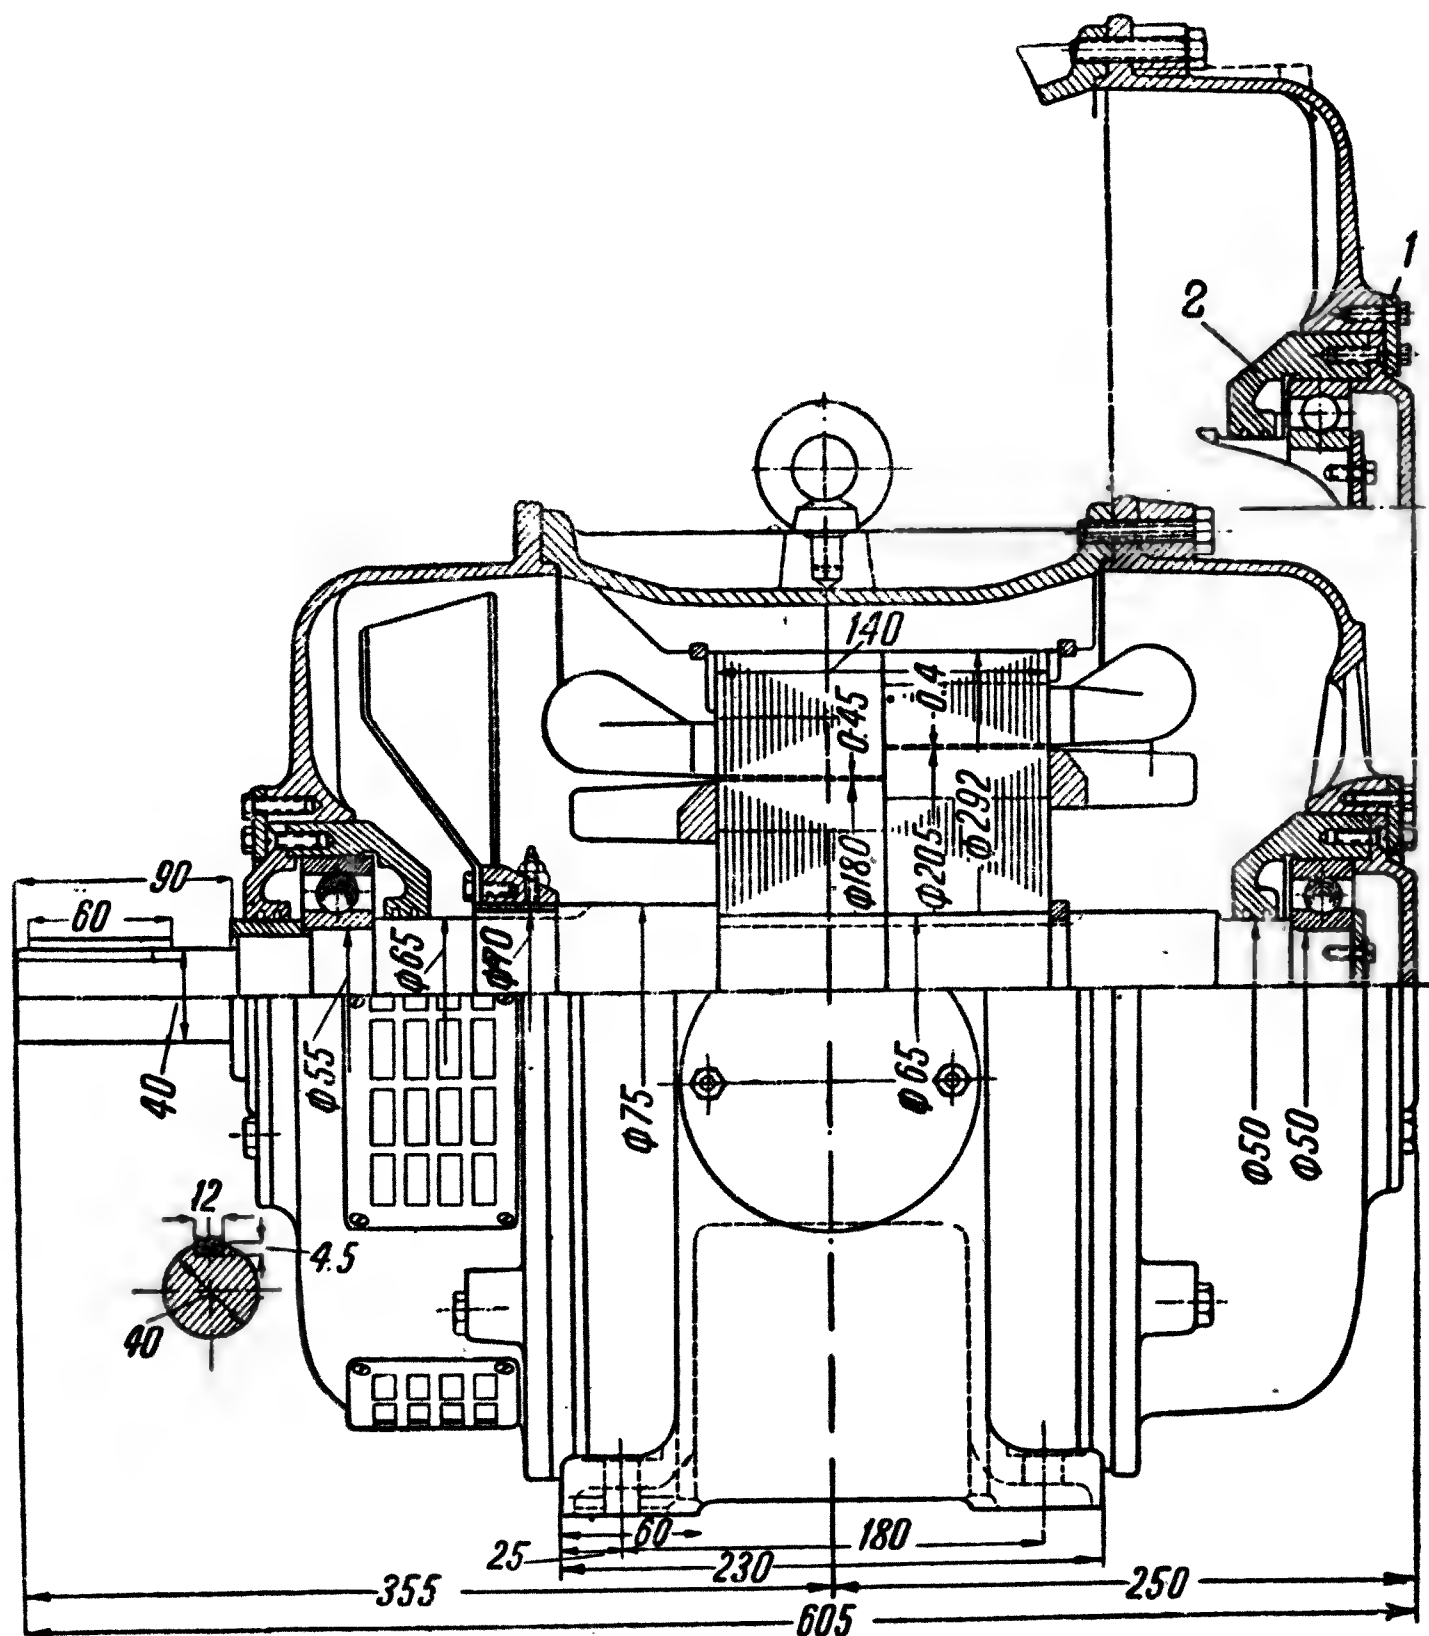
Асинхронный двигатель на шарикоподшипниках.
